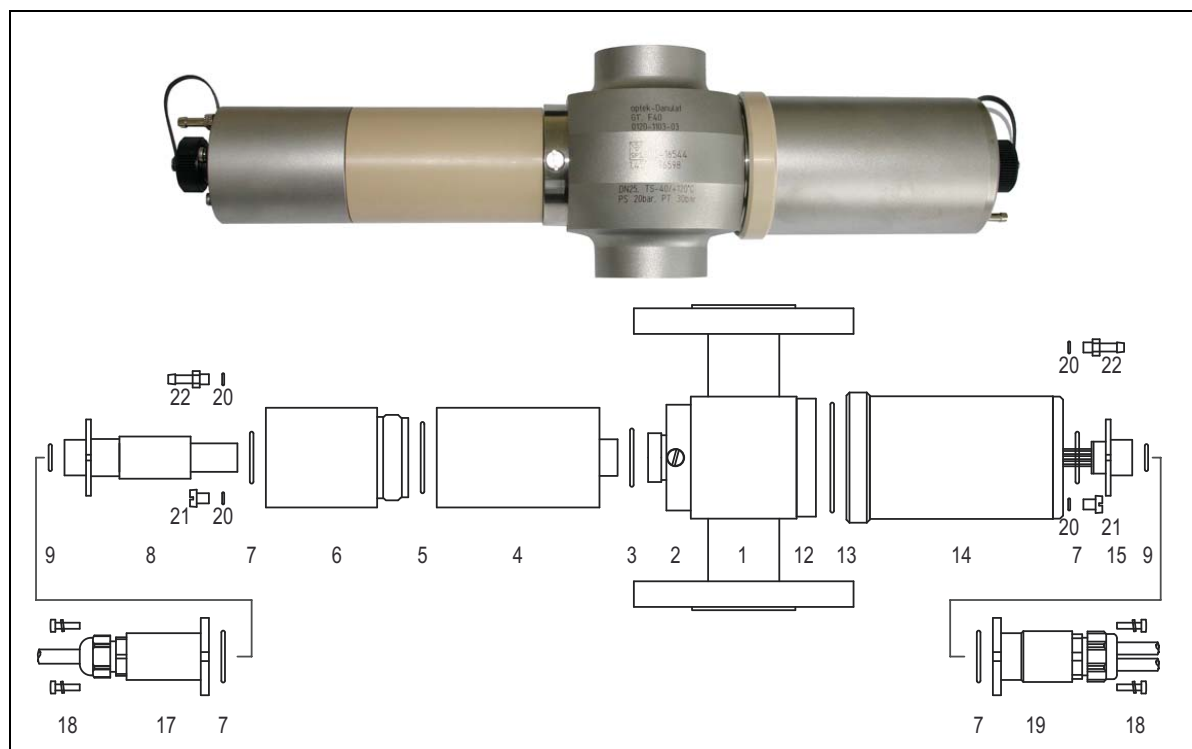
Foto y dibujo de despiece TF16-HT-PV / TF16-HT-PV-N
